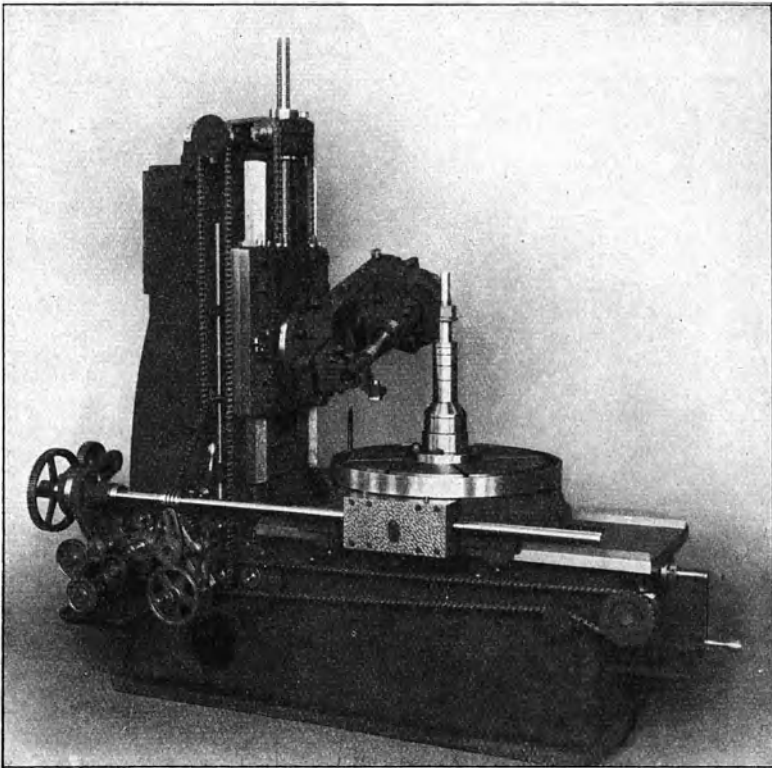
Die Räderfräsmaschine von H. Pfauter.
